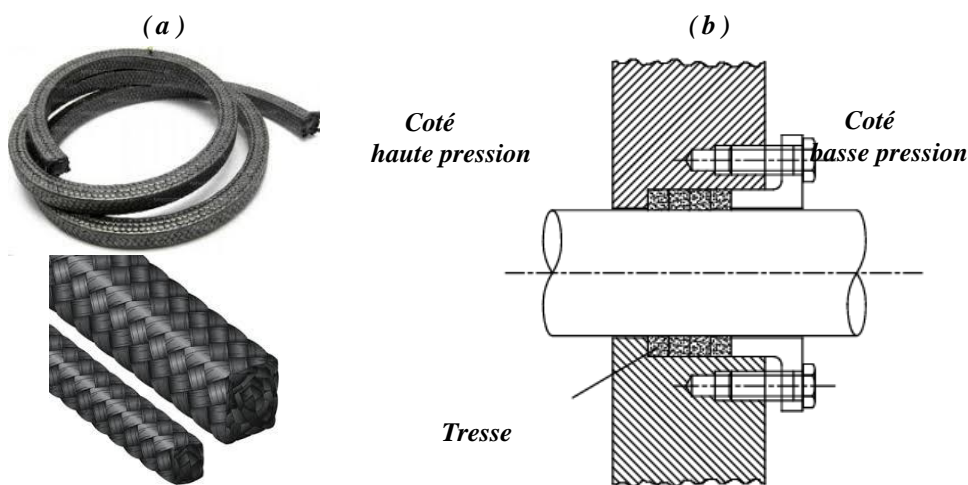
Étanchéité avec presse-étoupe en tresse : (a) Aspect extérieur d'une tresse, (b) Montage
